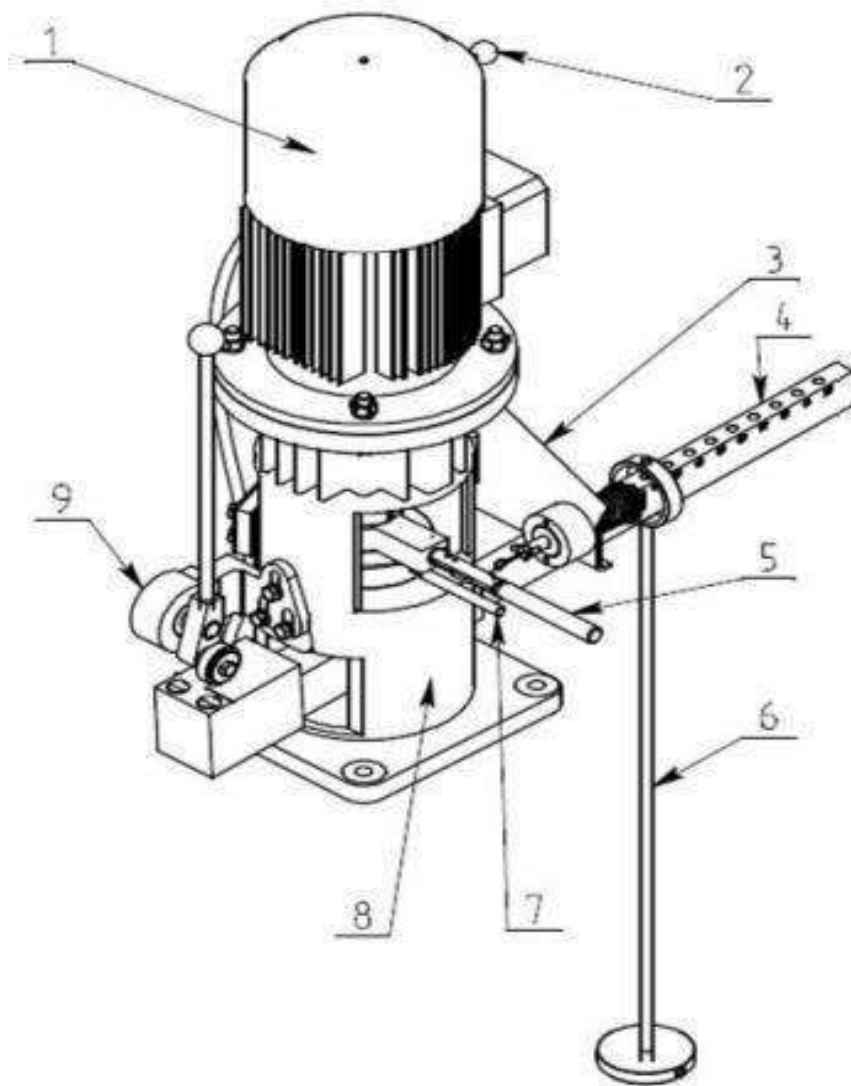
Вузол тертя: 1 – електродвигун; 2 – ручний механізм розгальмовування; 3 – обмежувач крутного моменту; 4 – важіль для створення осьових навантажень; 5 – корпус кріплення кульок; 6 – тримач гир; 7 – підставка під корпус; 8 – корпус вузла тертя; 9 – опора для прикладання та зняття осьових навантажень.
